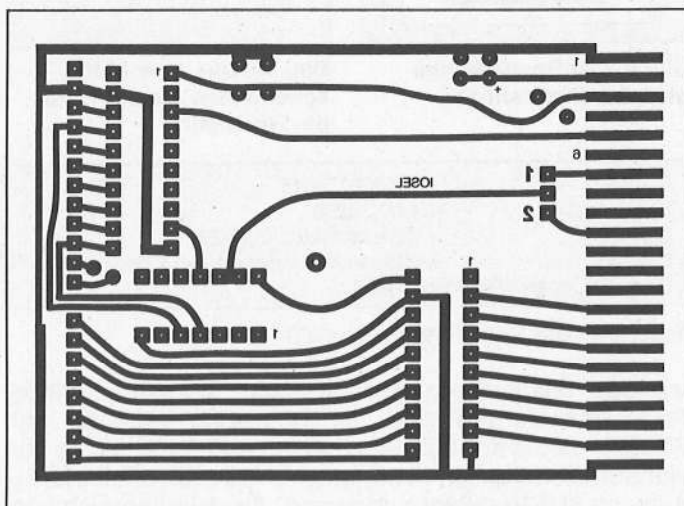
Layout für das I/O-Interface im Maßstab 1:1 (Bestückungsseite, spiegelverkehrt)
